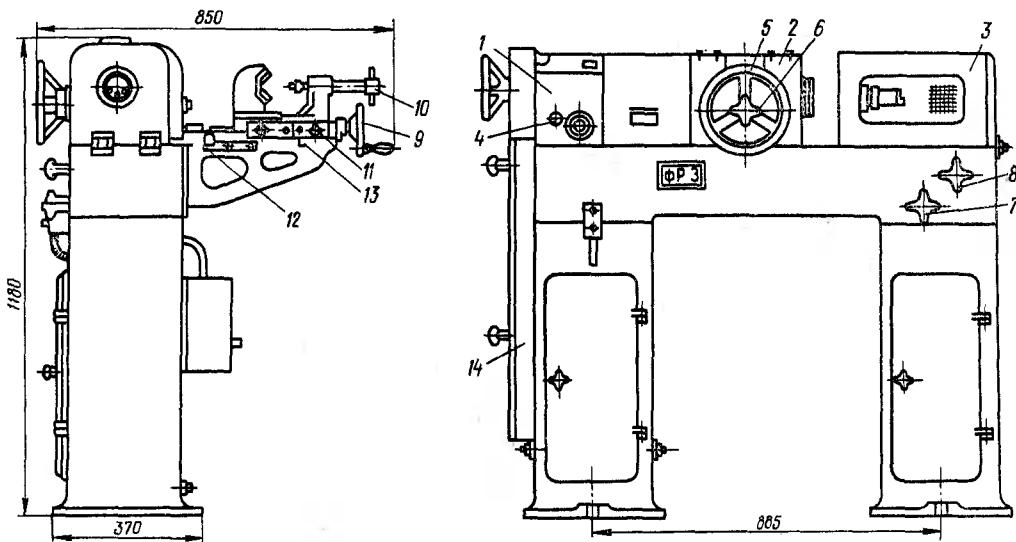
Общий вид станка УРБ-ВПМ:
